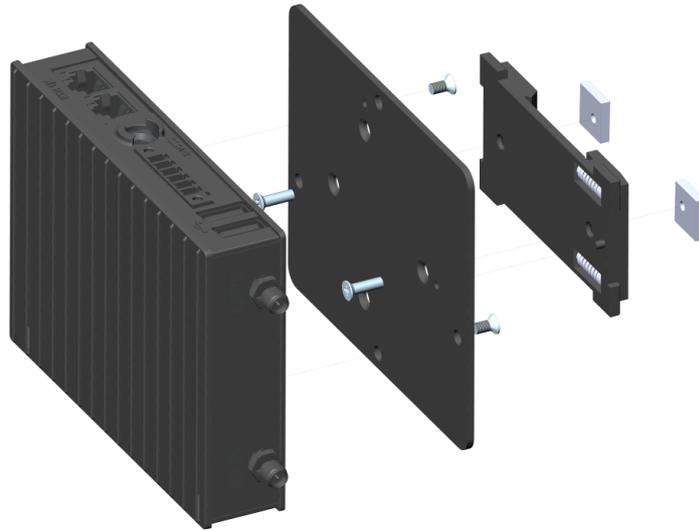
Fixação ED320 para trilho DIN (vista explodida)
